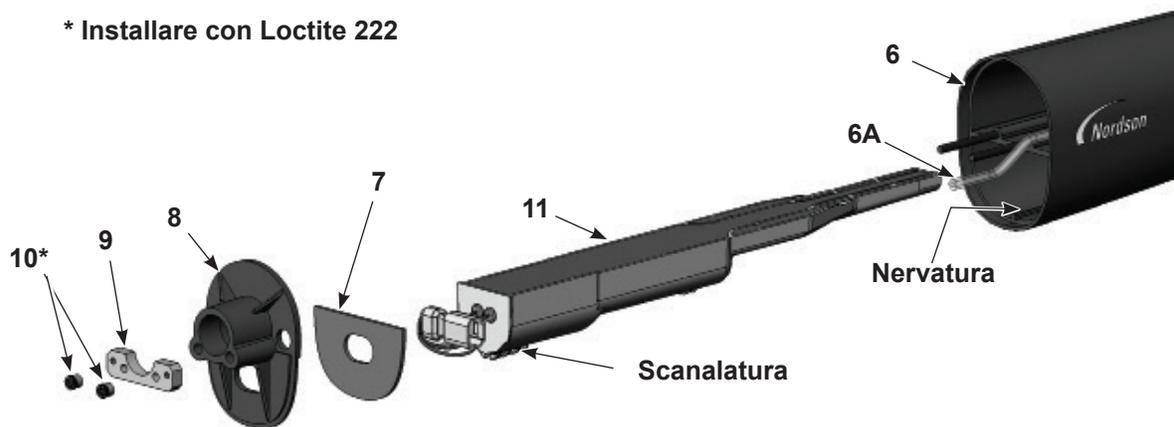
Smontaggio della pistola a spruzzo con montaggio su tubo 4 di 5
